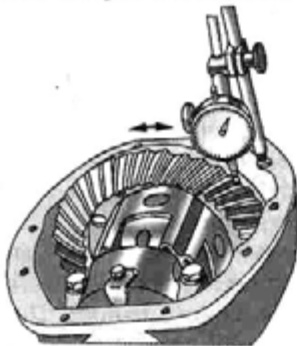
Проверка бокового зазора в зацеплении зубьев шестерен главной передачи (неразъемный задний мост)
